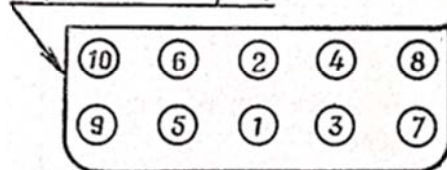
Порядок подтяжки гаек головки блока цилиндра
